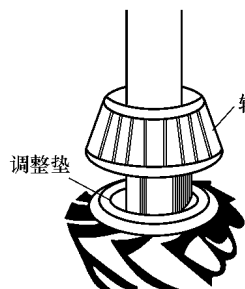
减速器主、从动齿轮啮合区调整垫的位置
